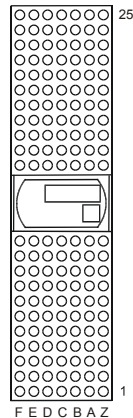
Steckverbinder X1 (Ansicht: Steckseite)
